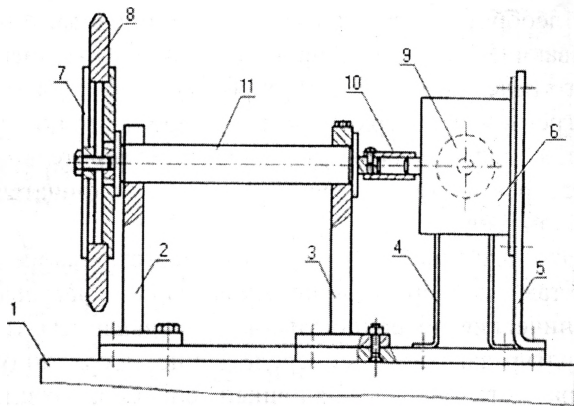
Привод вращения диска в процессе термической обработки: 1 — стол; 2 – 5 — опоры; 6 — редуктор; 7 — механизм крепления; 8 — диск; 9 — двигатель; 10 — соединительная муфта; 11 — вал
